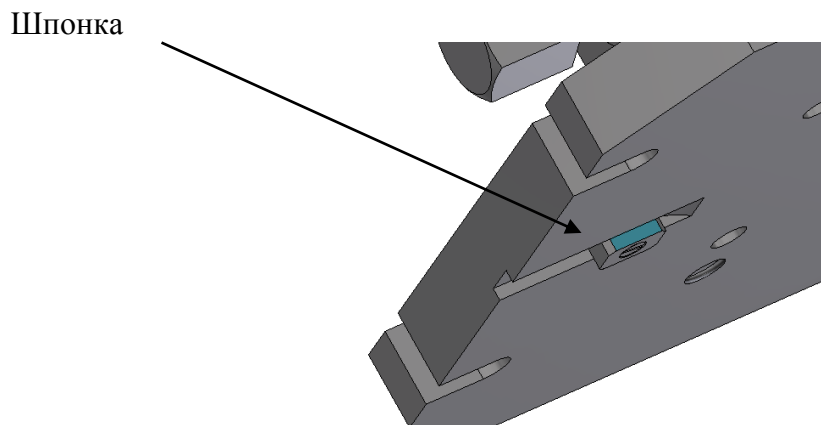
Шпонка, закрепленная на основании приспособления, предназначенная для установки приспособления на столе станка
